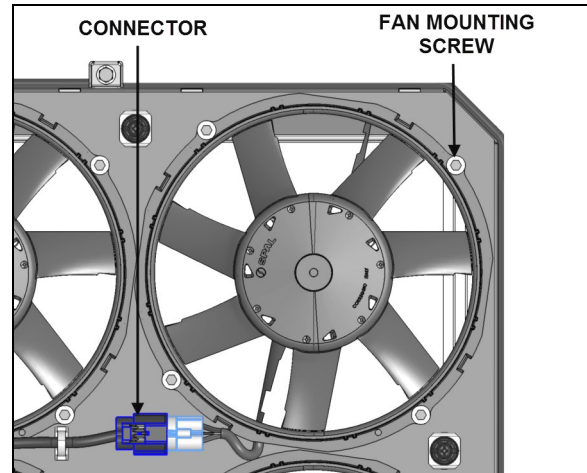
LOCALIZACIÓN DE CONECTOR & TORNILLOS DE MONTAJE
